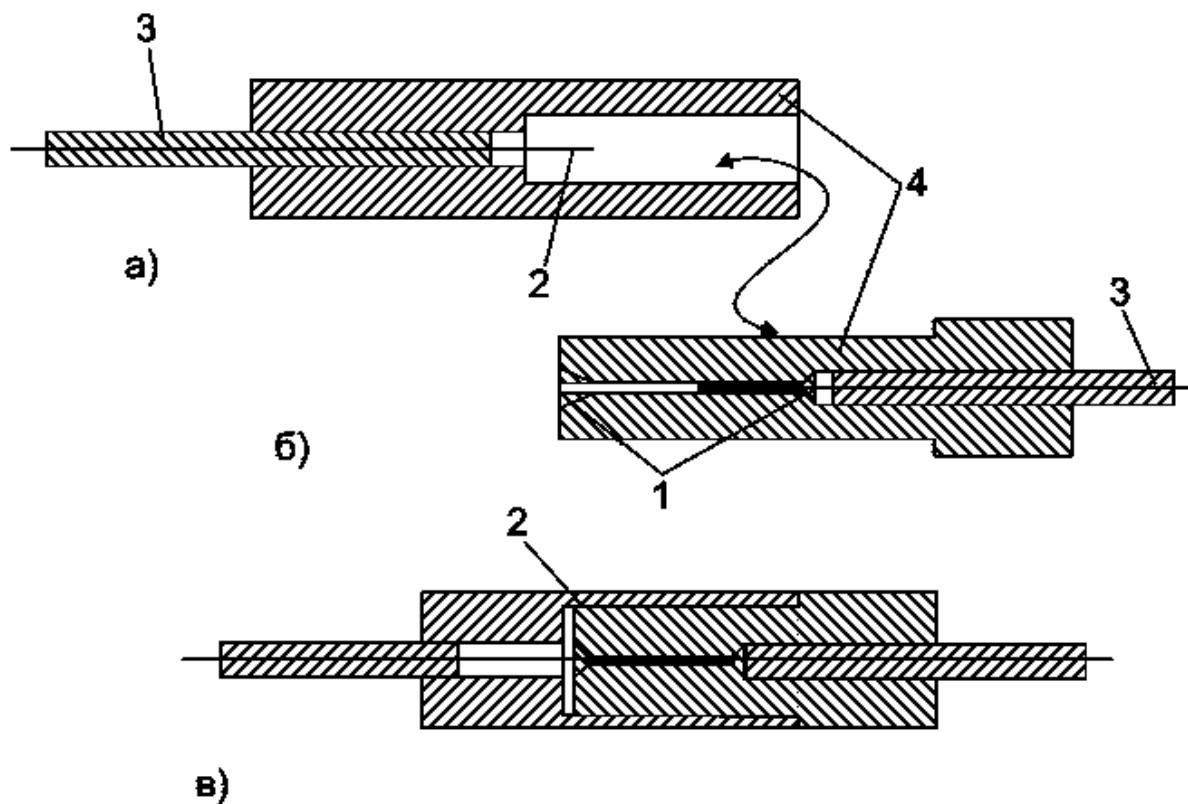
Штекерне з'єднання: а) гніздова частина; б) штирєва частина; в) зросток; 1 – канал; 2 – волокно; 3 – сталеві трубки; 4 – з'єднані поверхні
